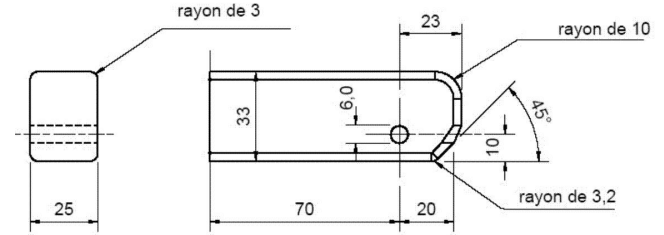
Vue de l'arrière et de côté du dispositif de contrôle pour le système d'attaches inférieures — Dimensions de l'enveloppe
